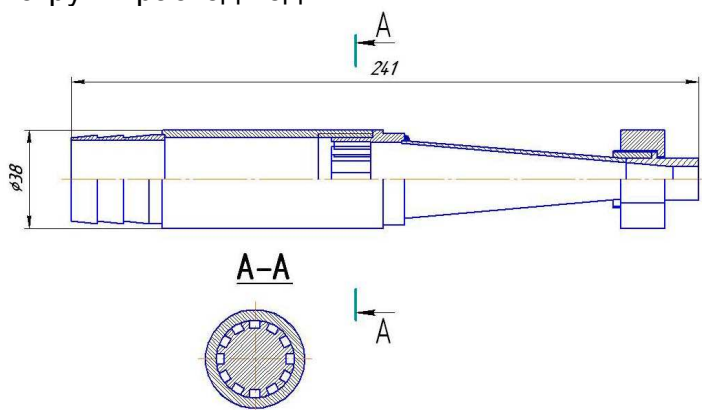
Конструктивная схема однофазного струйно-центробежного распылителя
